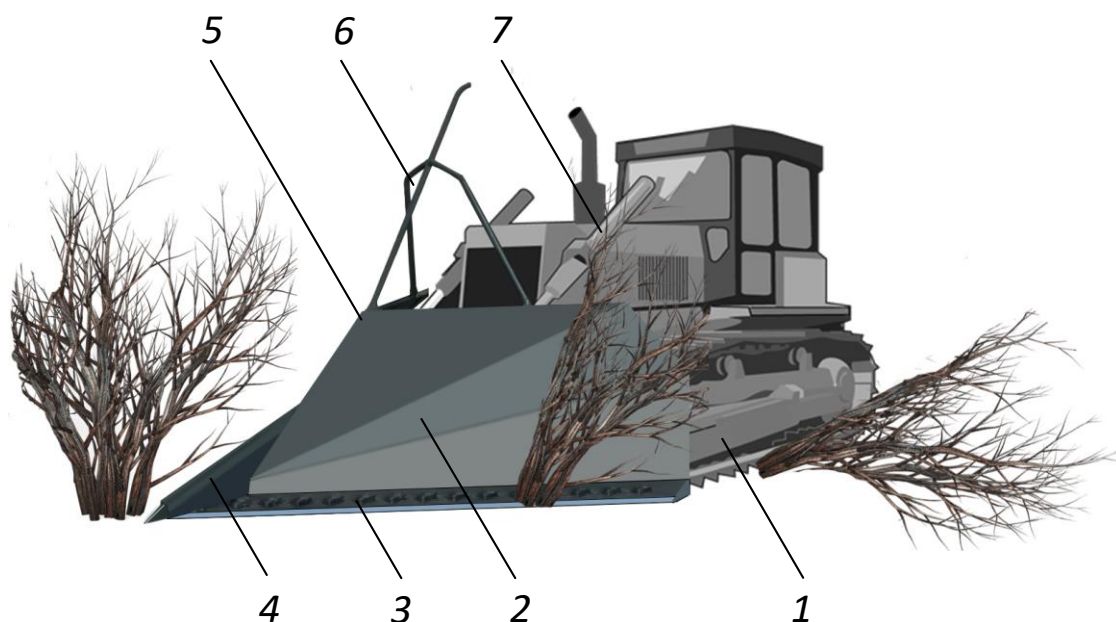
Конструктивна схема кущоріза: 1 – рама; 2 – полиця; 3 – ніж; 4 – клин-колун; 5 – корпус; 6 – огороження; 7 – гідроциліндр
